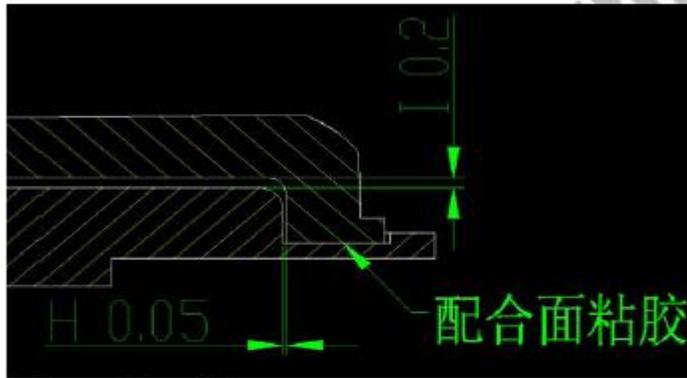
SIDE_KEY 与 SIDE_KEY_RUBBER 装配定位尺寸图
